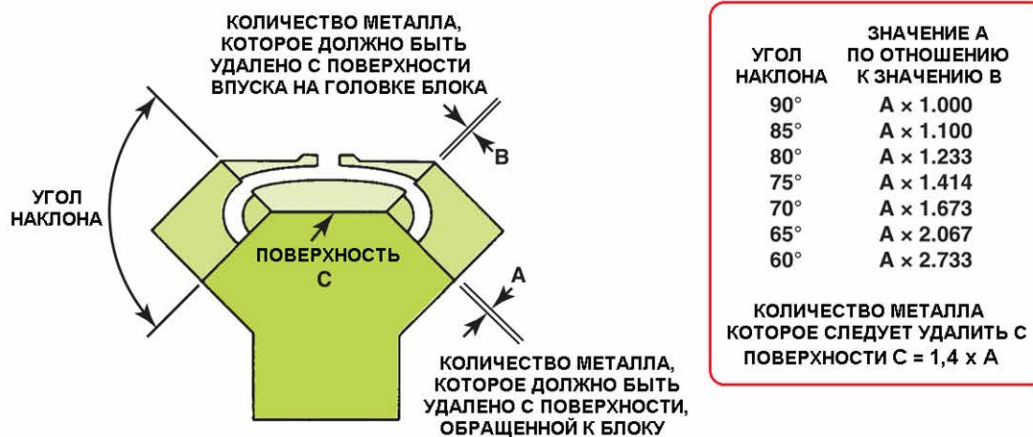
Материал, который должен быть удален с привалочной поверхности впускного коллектора, зависит от угла между привалочными поверхностями прокладки головки цилиндра и прокладки впускного коллектора, и толщины материала, снятого при шлифовке головки цилиндра; источник: *Pearson Education, Inc.
